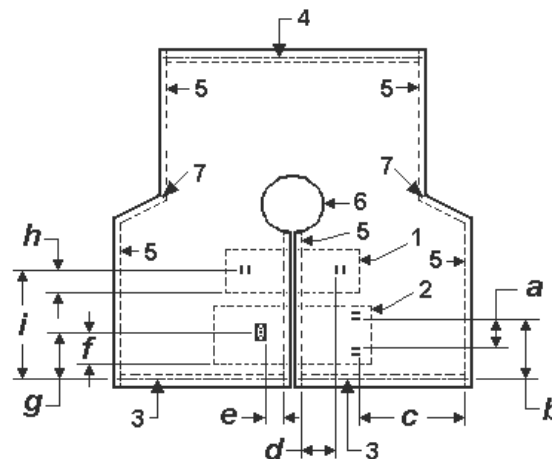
Conjunto de tira pectoral (parte ajustable izquierda y parte fija derecha)
